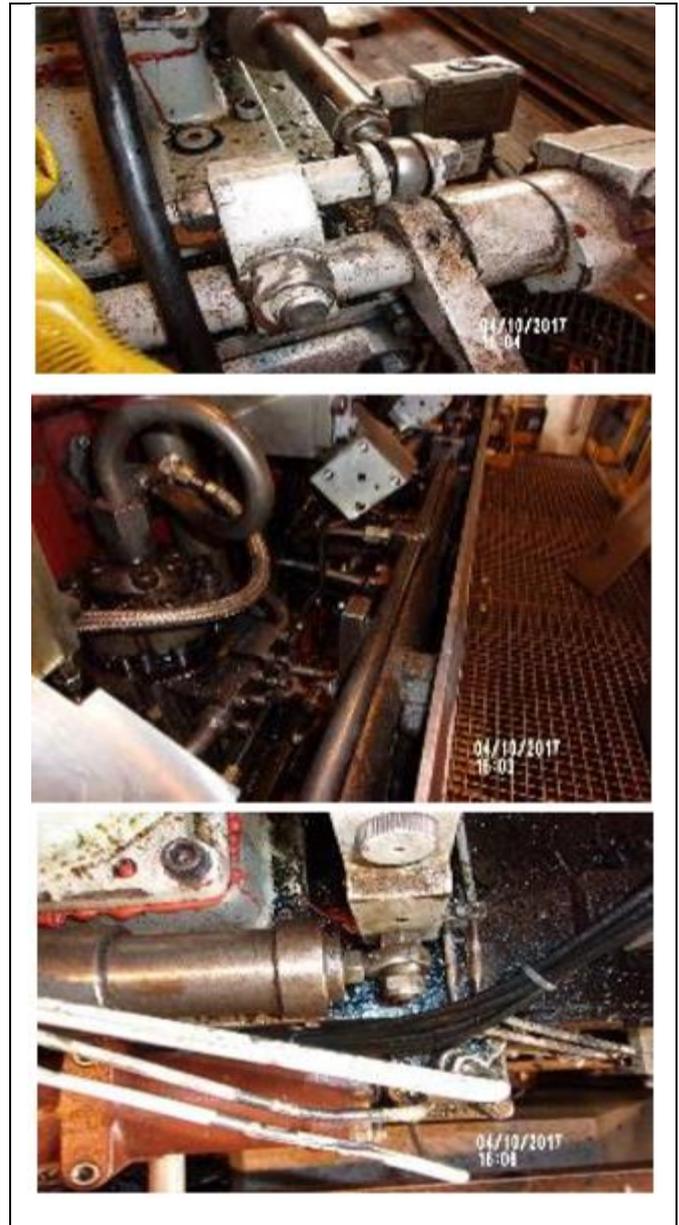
Sistema de inspeção no sistema de bomba injetora.
